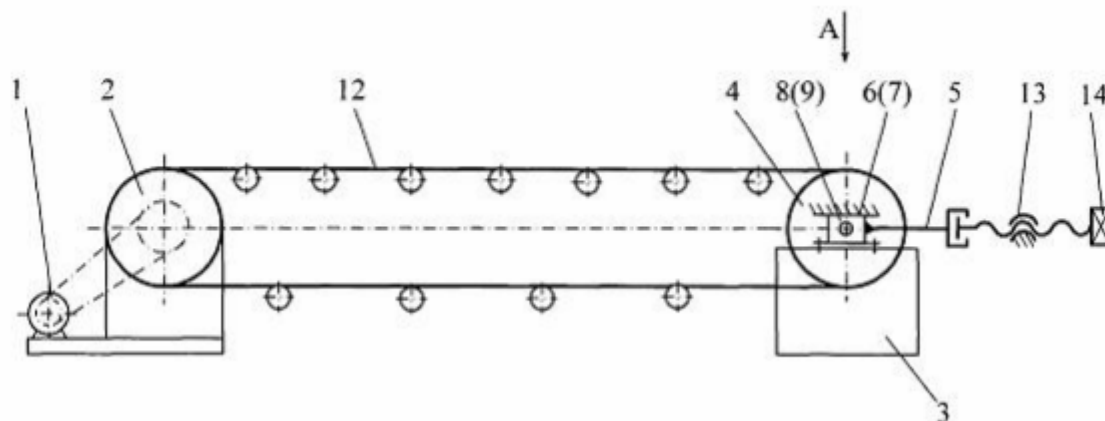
Натяжний пристрій стрічкового конвеєра
